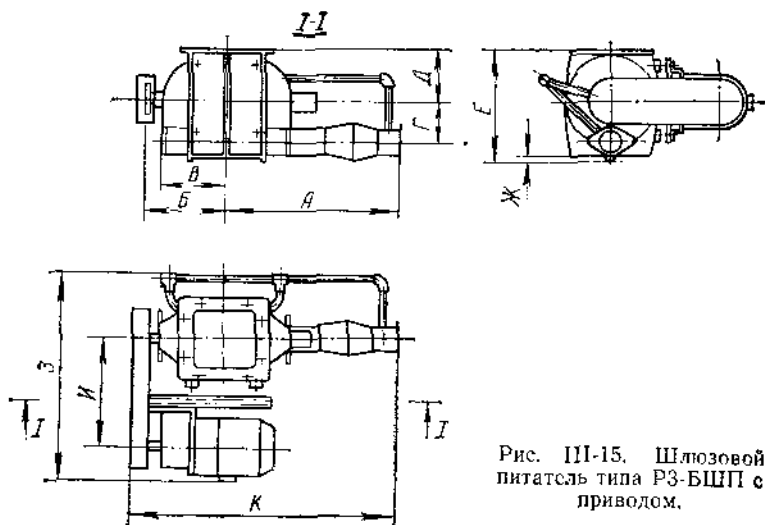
Шлюзовой питатель типа РЗ-БШП с приводом.
